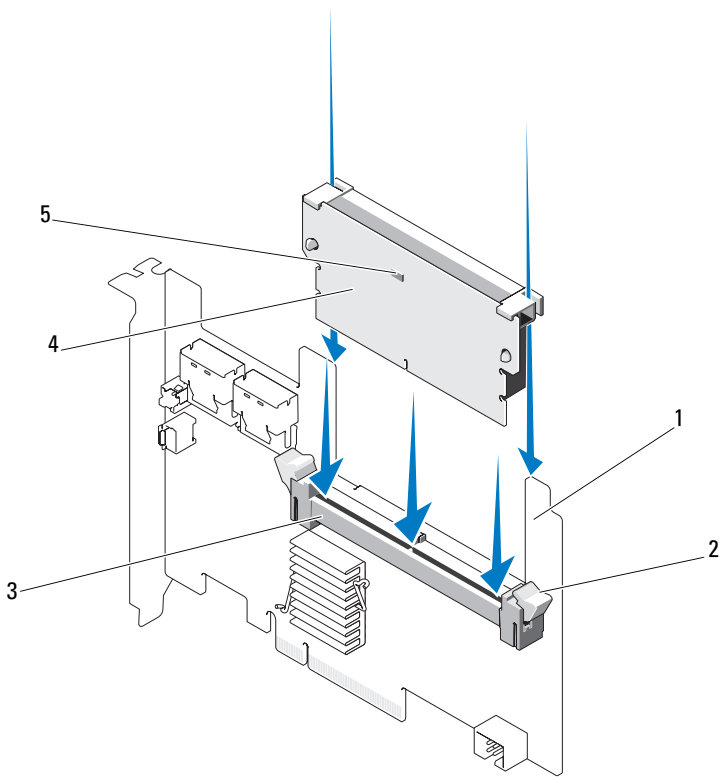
Montaje del soporte del DIMM en el DIMM
